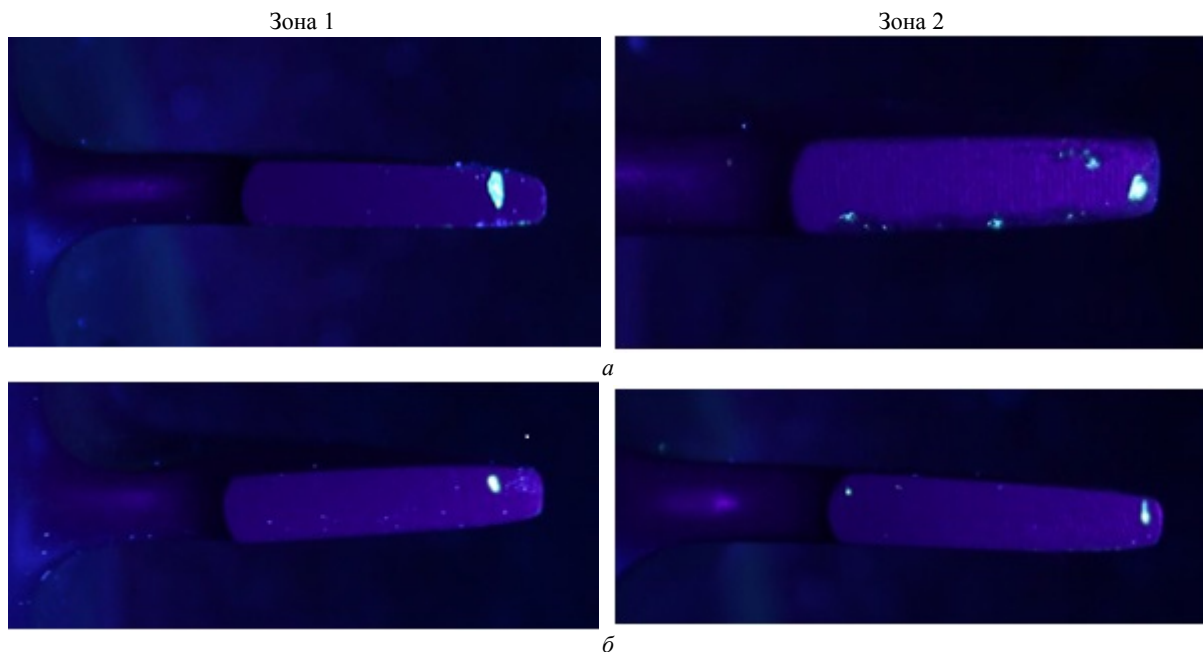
Вид изделия с индикаций при контроле ЛЮМ1-ОВ: а – аргонодуговая наплавка; б – лазерная наплавка
